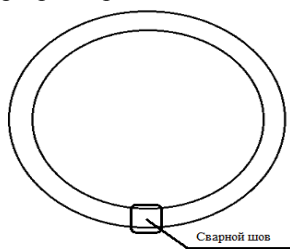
Образец на растяжение сварного соединения до испытания
